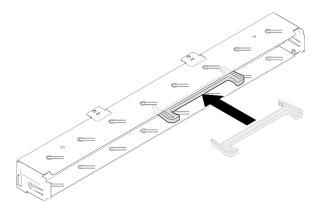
Befestigen der magnetische Seite des Werkzeugs am Gehäuseinneren
